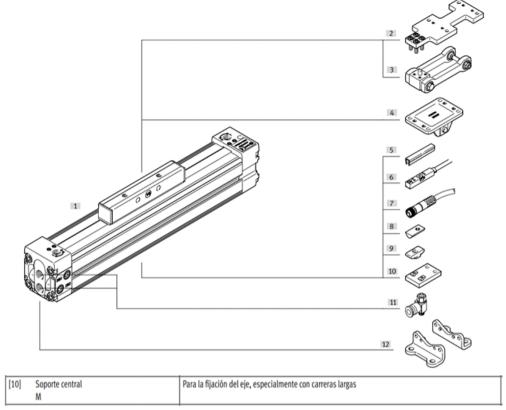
s: Accesorios cilindro vertical-soporte central
